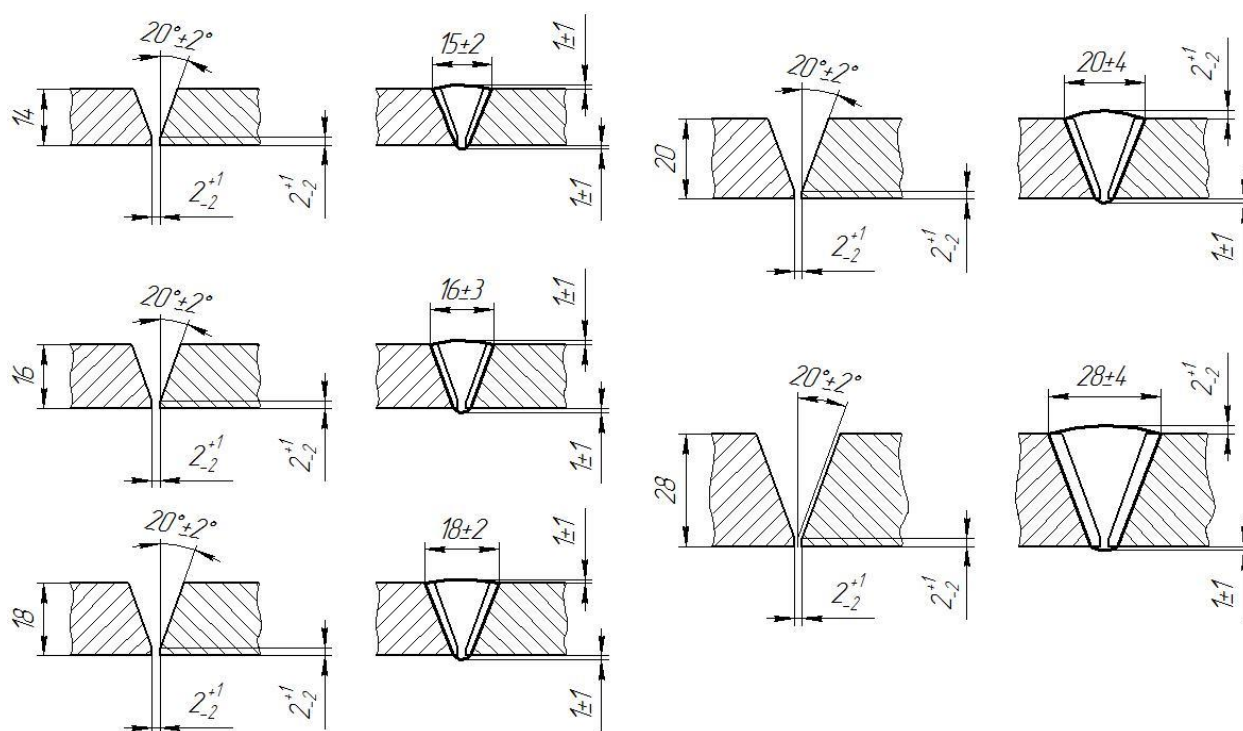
Разделка кромок и форма шва для стыкового соединения при укрупнении листовых заготовок
